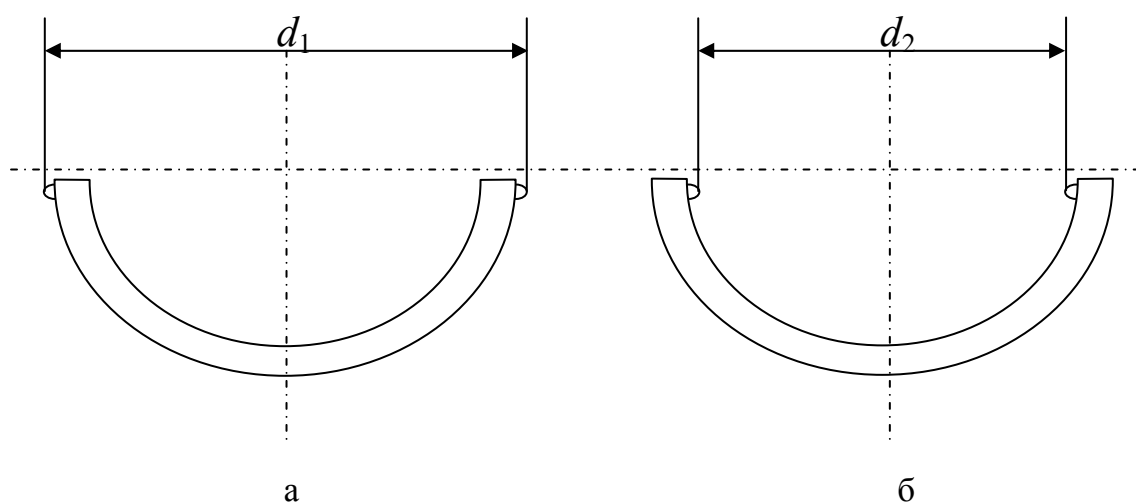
Схема измерений размера вкладыша в месте разъема: а - свободный вкладыш; б - вкладыш при запрессовке в шатун.
